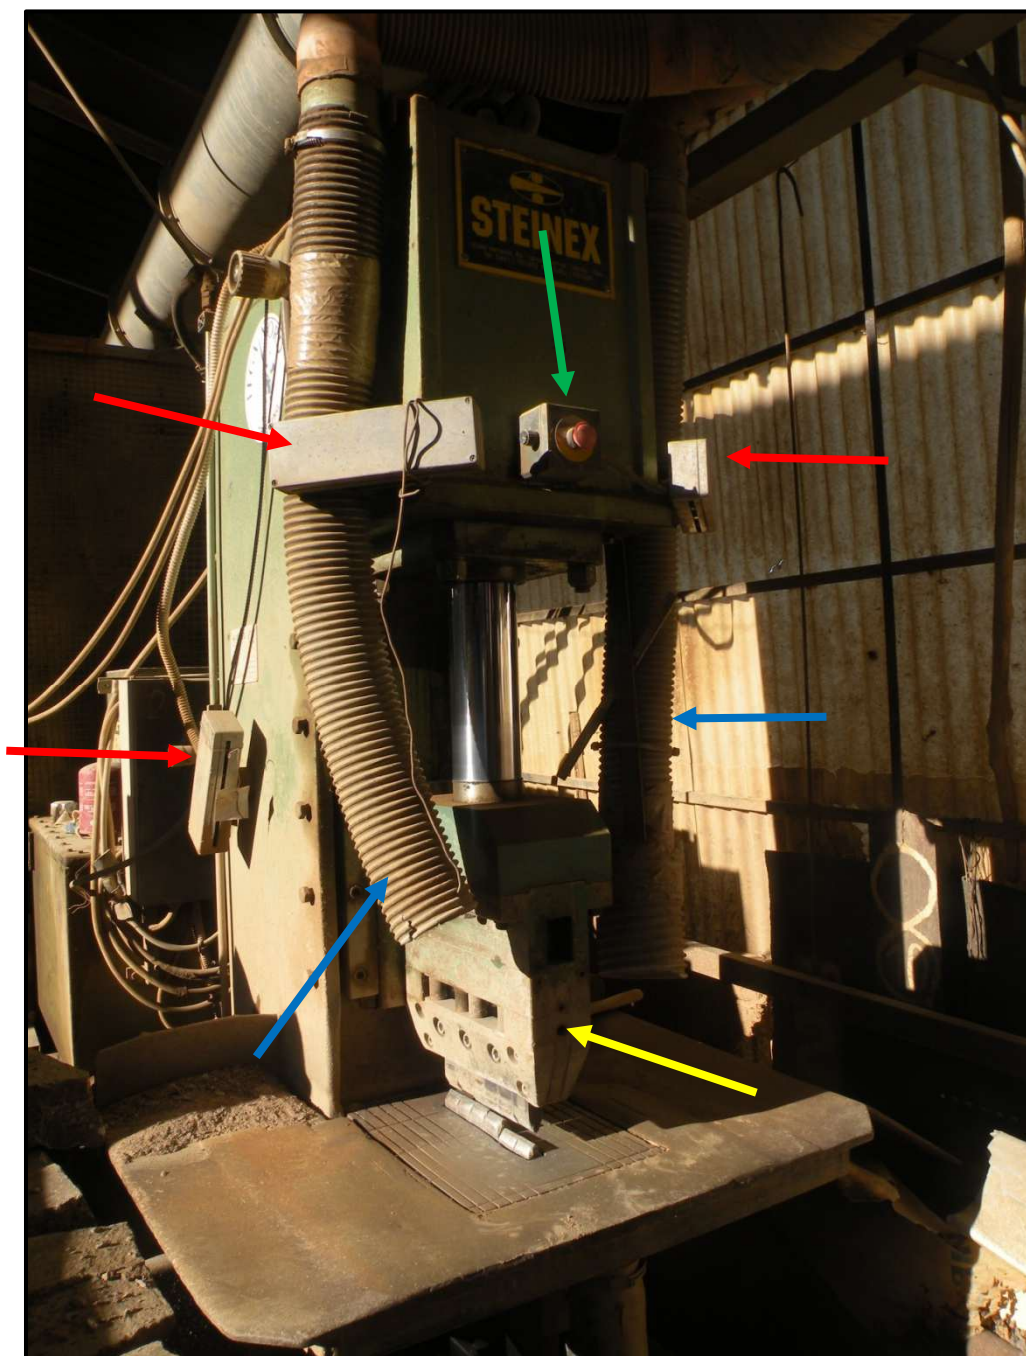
Macchina a spacco per la realizzazione di cubetti e/o piastrelle
